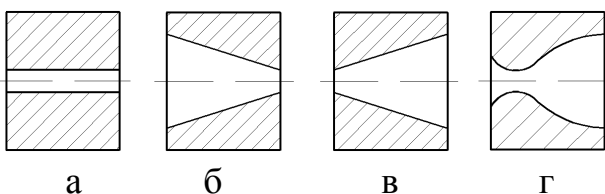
Сопла для абразивної обробки затопленими струменями:
